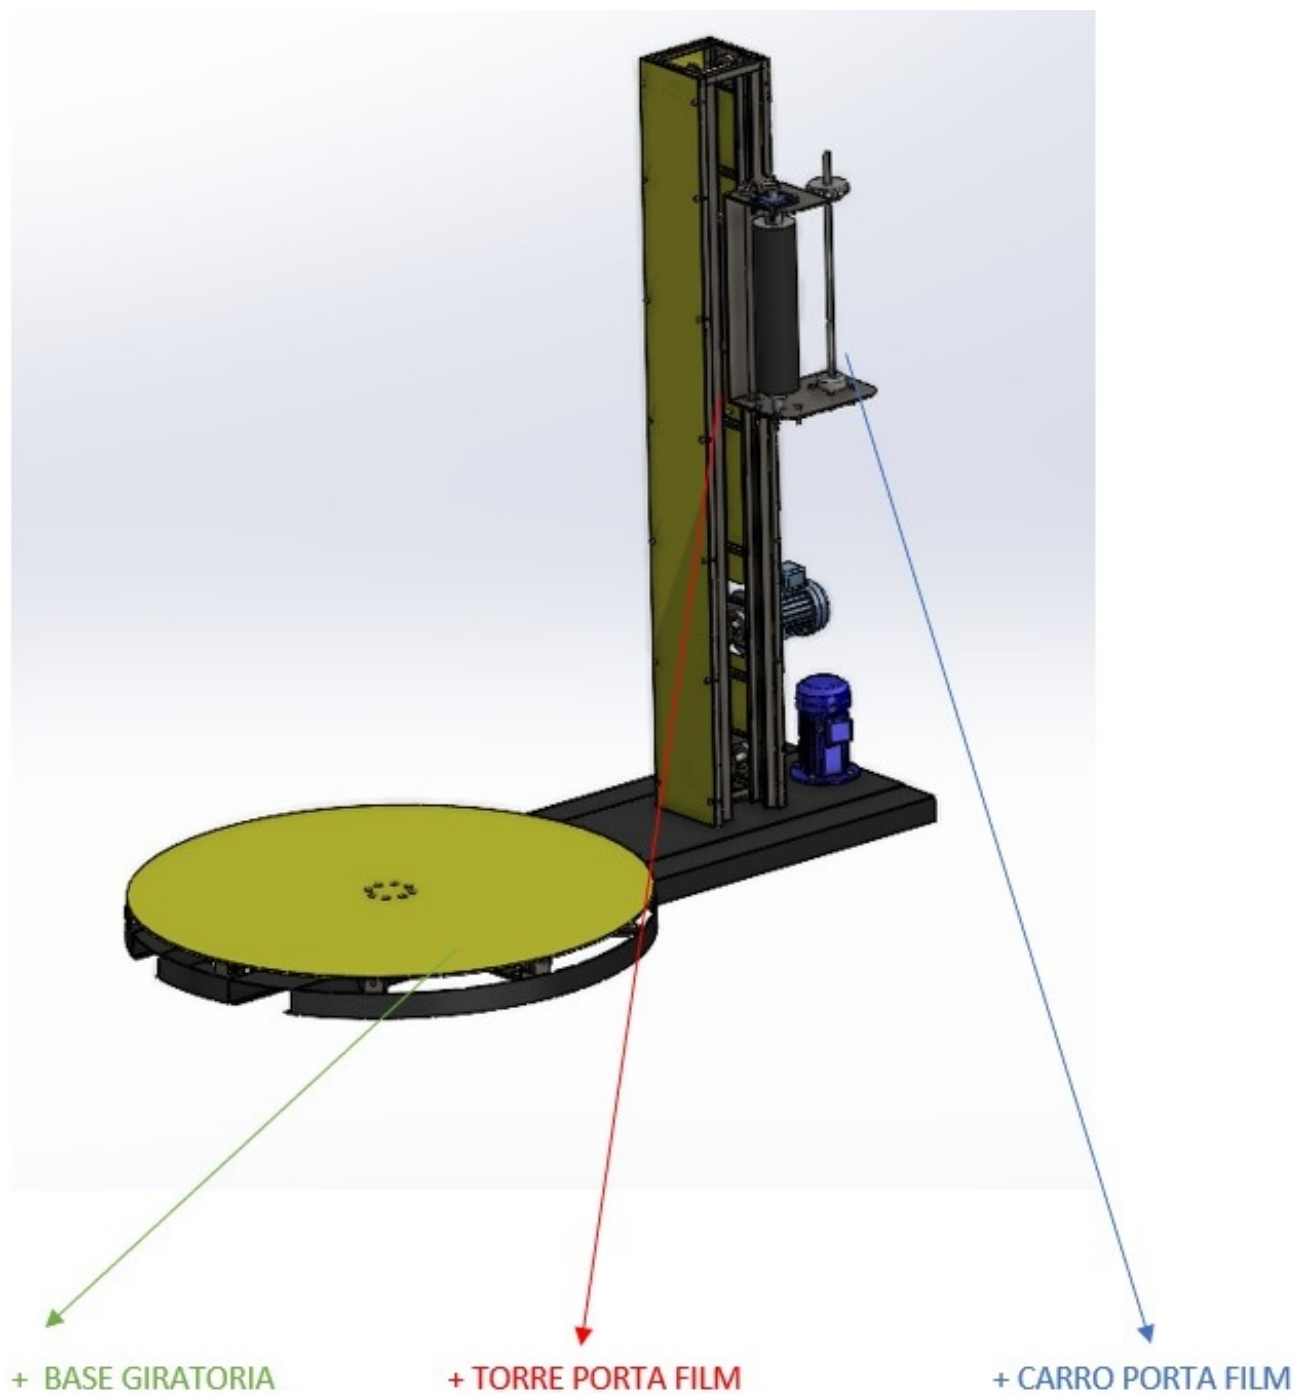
Diseño máquina embaladora automática. Fuente: Autoría Propia
